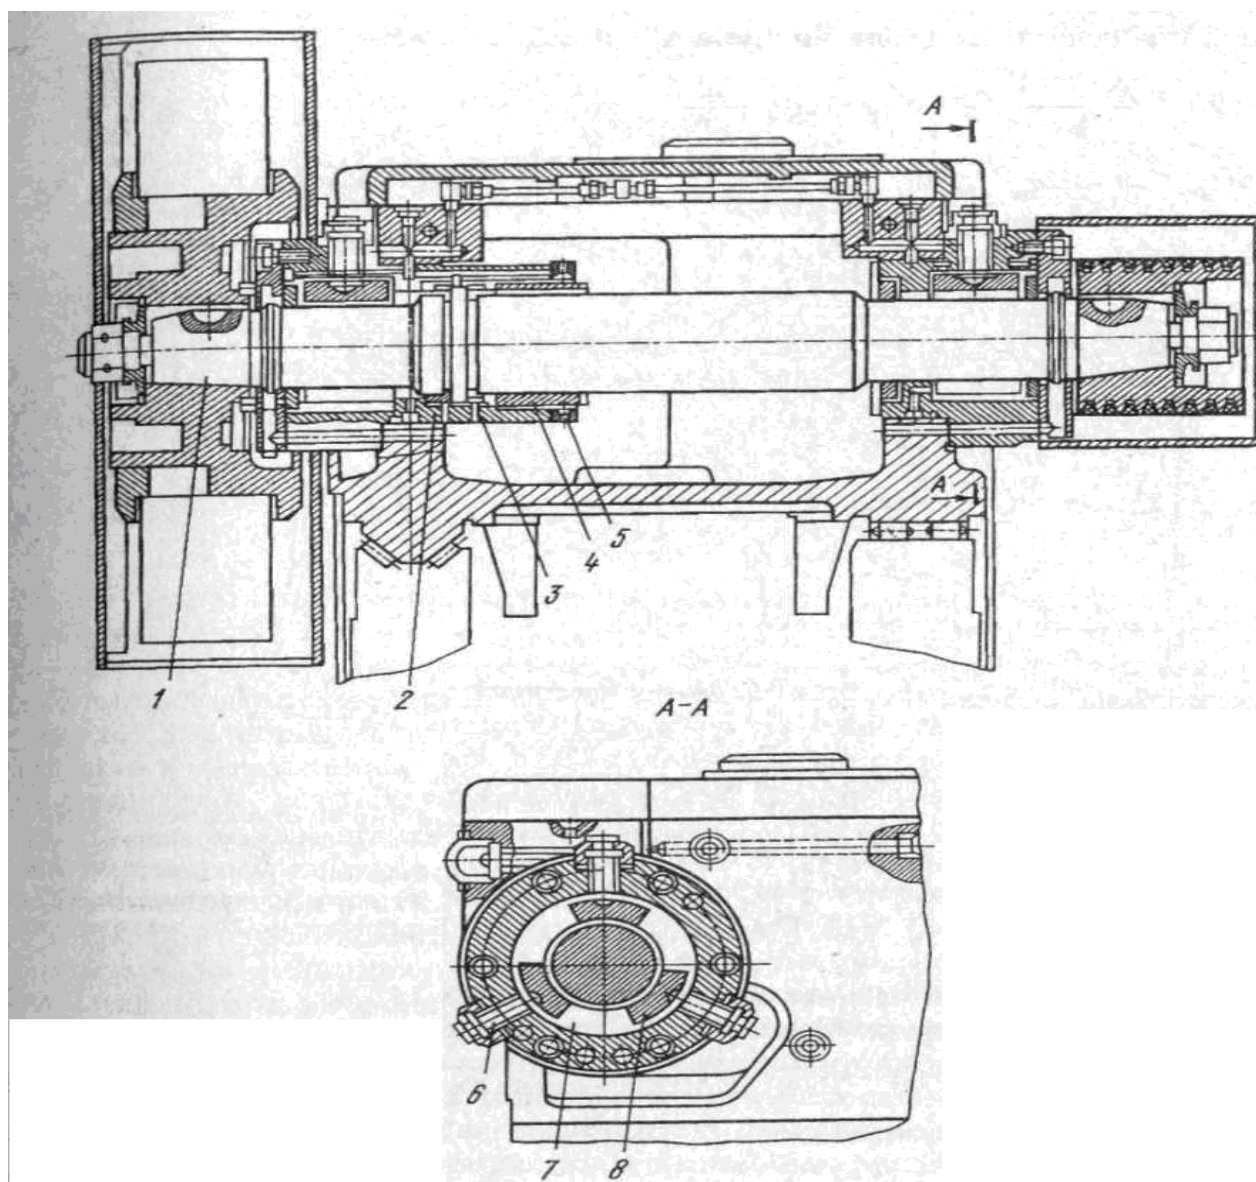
Шлифовальная бабка станка модели 3М121: 1 – шпиндель, 2, 3 – сферические шайбы осевой фиксации шпинделя, 4 – гайка, 5 – контргайка. 6 – винты, 7 – масляный клин, 8 – вкладыши..
